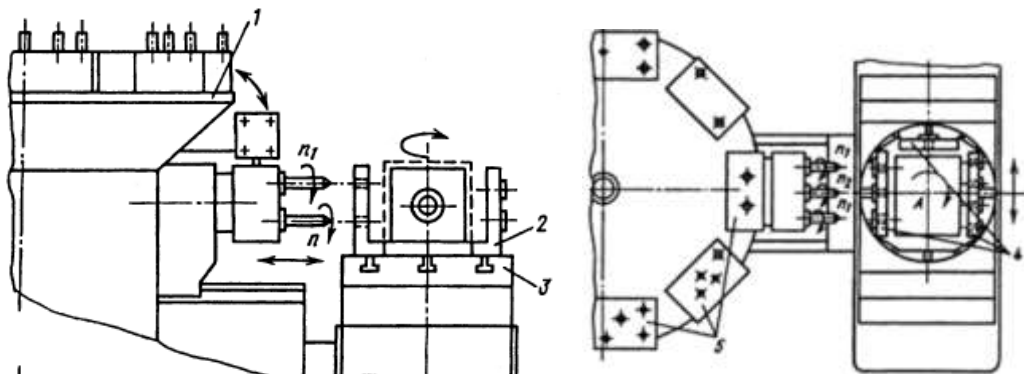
Верстат з ЧПК мод. ХПА4 з автоматичною зміною багатшпindelних головок та здатністю до переналагодження. Позначено: 1 – магазин із змінними шпindelними коробками; 2 – пристосування-супутник; 3 – поворотний стіл; 4 – вузли спрямування інструментів; 5 – змінні шпindelні коробки [39].
